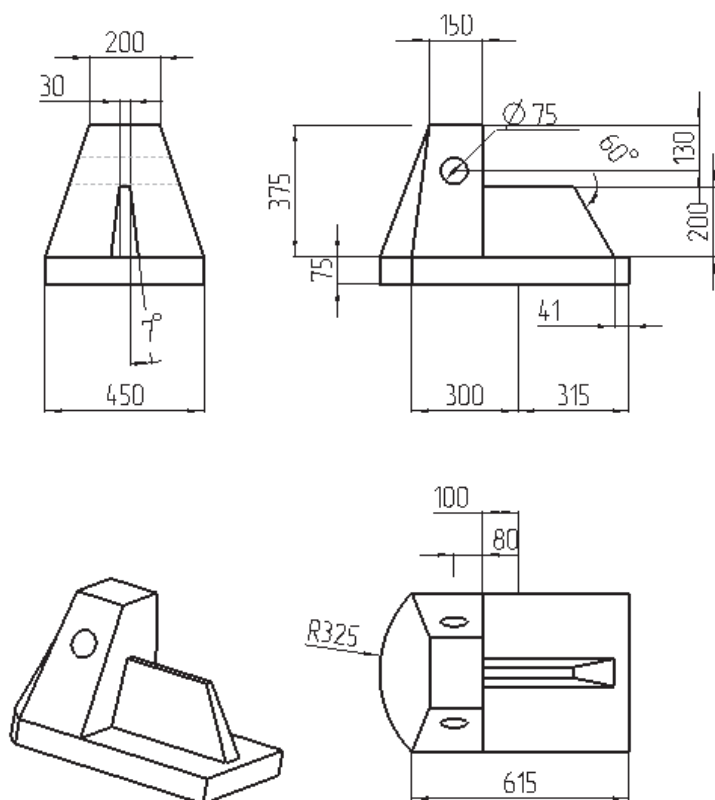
Общий вид и габаритные размеры модели опоры
